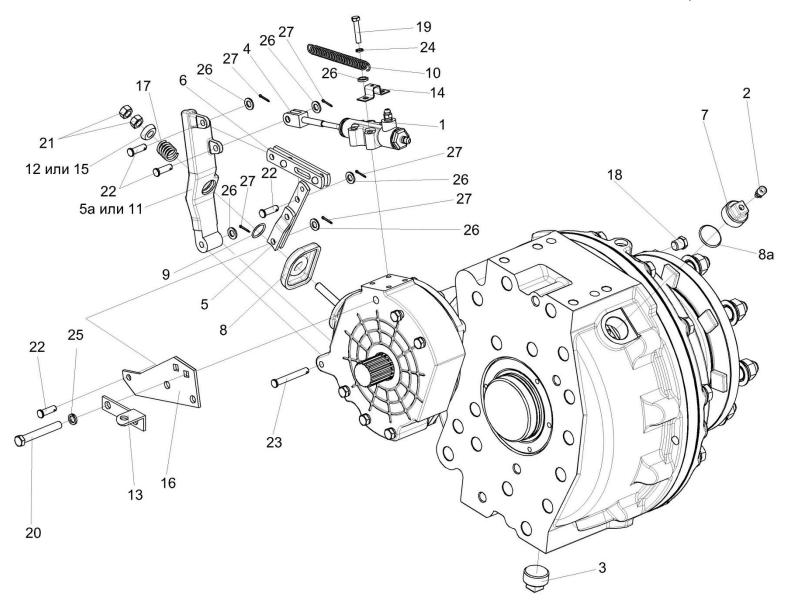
Редуктор бортовой правый УЭС 0107070А-04 (лист 1)
